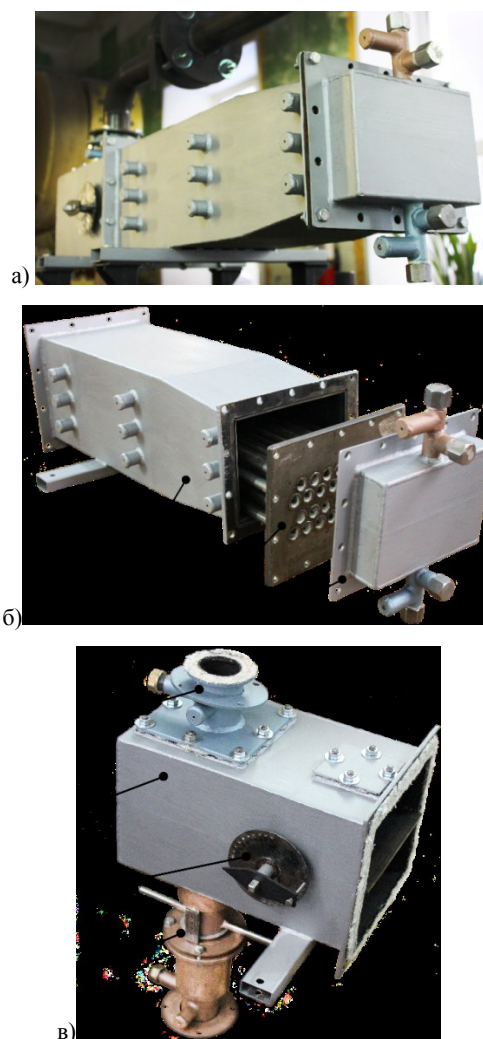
Конструкция опытного образца компактного котла-утилизатора: а) опытный образец компактного котла-утилизатора в сборе; б) теплообменная часть опытного образца компактного котла-утилизатора: 1 – передняя водяная камера; 2 – теплообменная секция; 3 – корпус теплообменной секции; в) перепускная часть опытного образца компактного котла-утилизатора: 1 – входной патрубок; 2 – устройство регулирования положения газовой заслонки; 3 – корпус перепускной части; 4 – выходной патрубок
